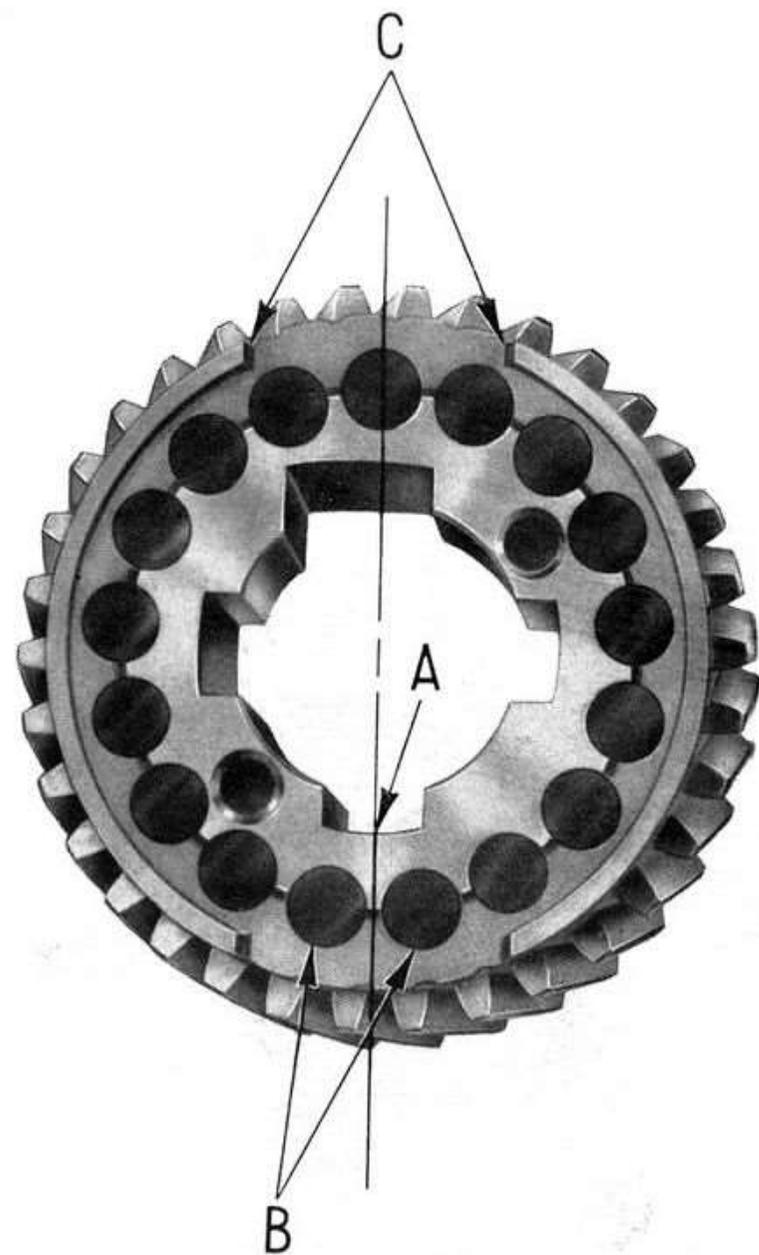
Come viene montato il corpo interno del pignone elastico motore.
